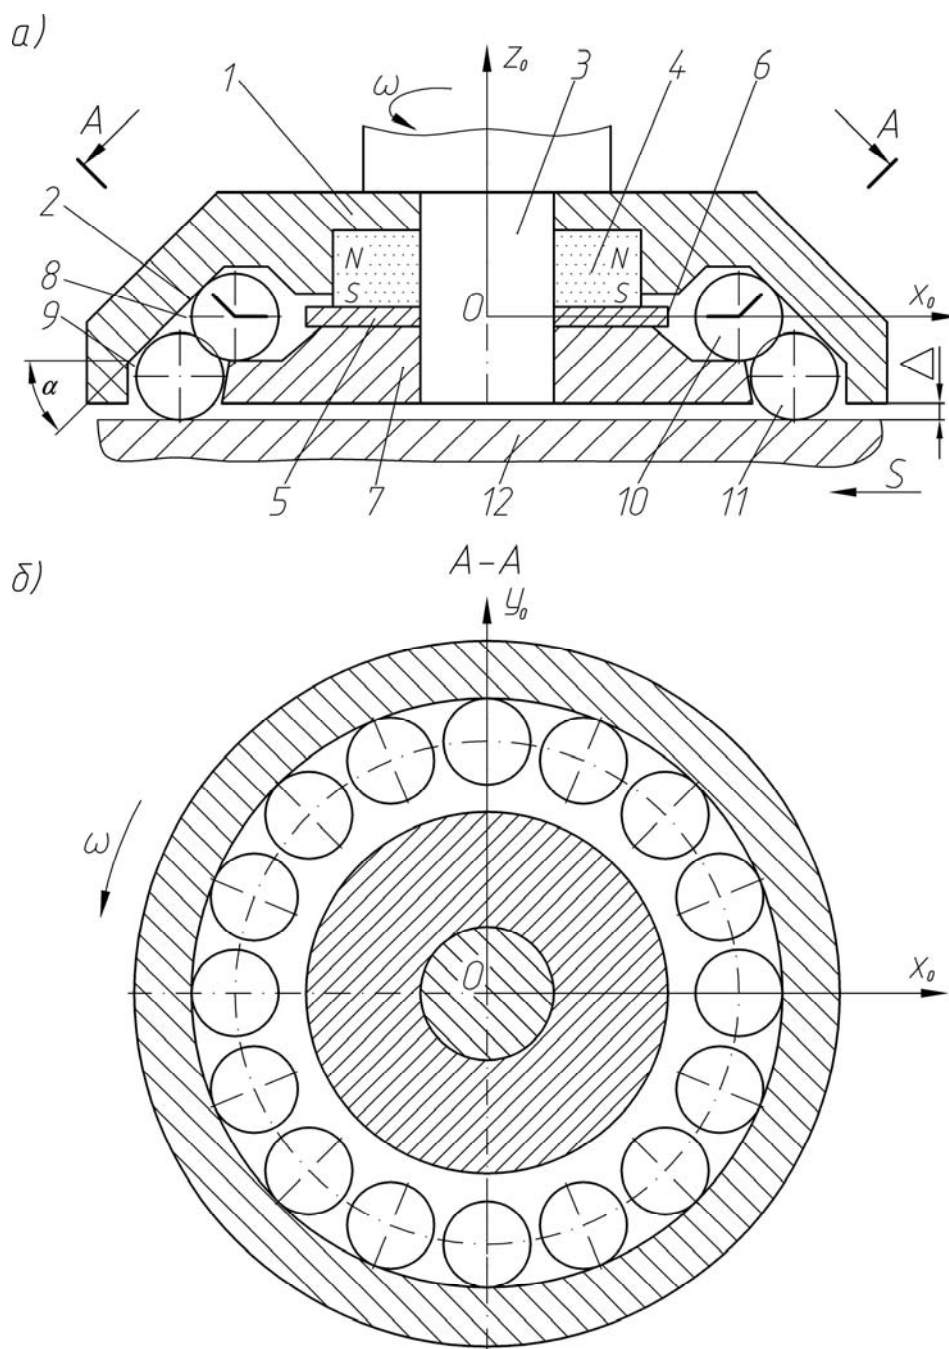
Схема инструмента для магнитно-динамического упрочнения плоских поверхностей: а – общий вид схемы; б – поперечное сечение инструмента
